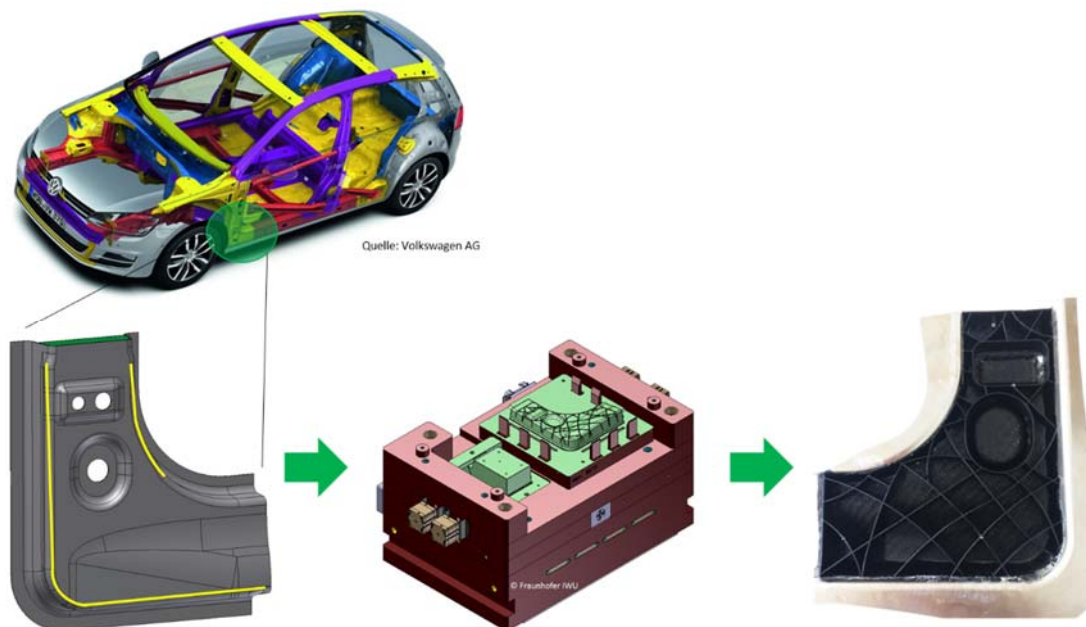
Demonstrator A-Säulenschuh mit der unteren Werkzeughälfte
